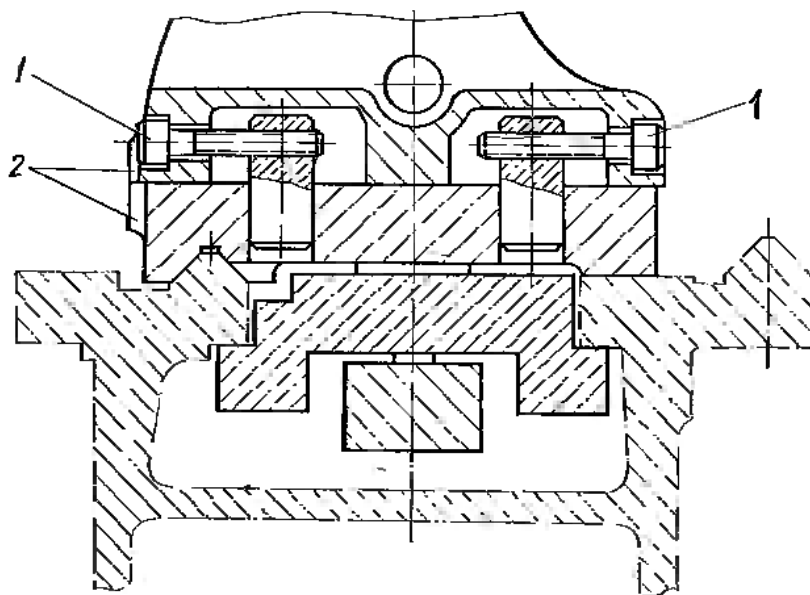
Эскиз смещения корпуса задней бабки с линии центров при точении конусов
